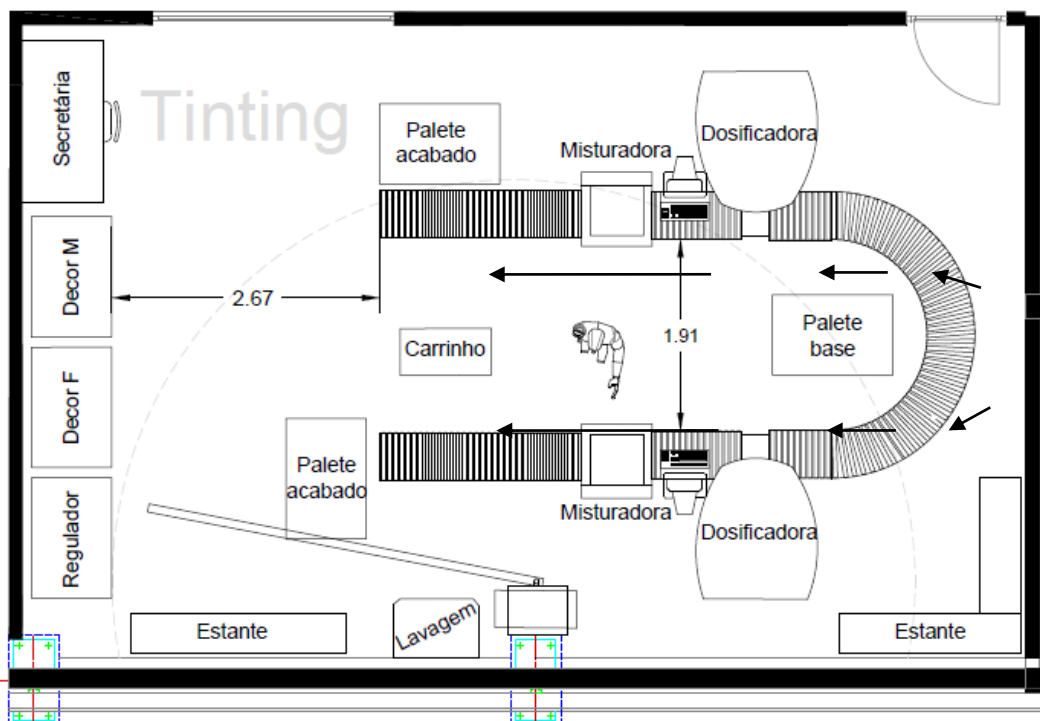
Layout proposto para duas linhas de Tinting no centro de Aveiro.
